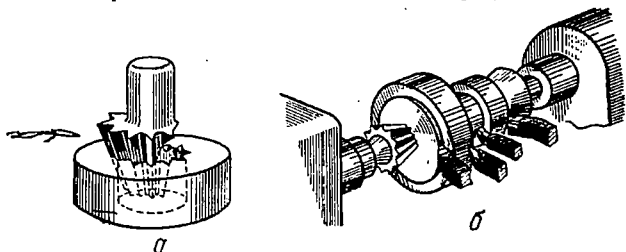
Приспособление для черновой обточки шестерен на рифленной оправке:
